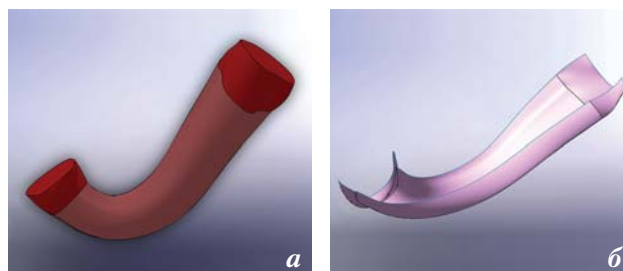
3D-модель шаблона для СИ (а) и заготовки для изготовления СИ (б).
